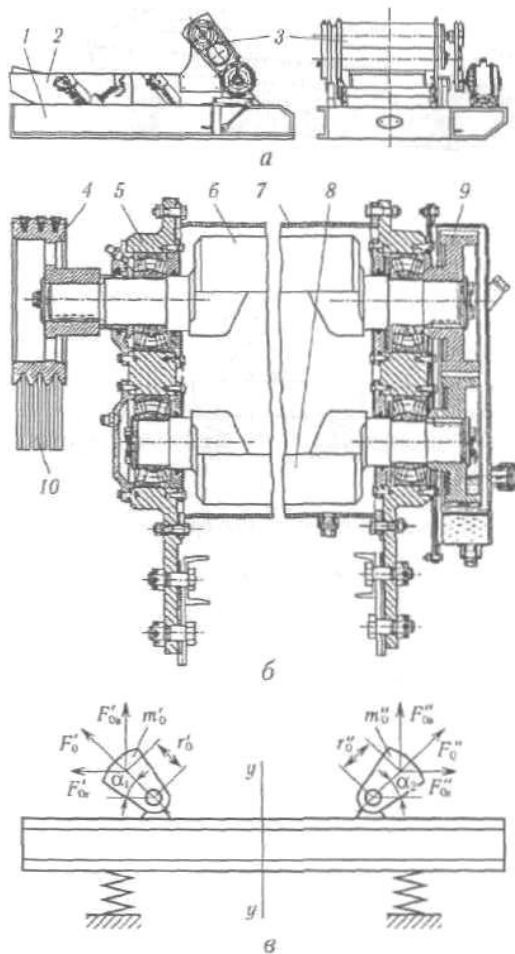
Горизонтальний грохот із напрямленими коливаннями: а – загальний вигляд; б – вібробудувач; в – схема вібробудувач, встановленого на коробі грохота, 1 – корпус; 2 – короб; 3 – вібробудувач напрямленої дії; 4 – шків; 5 – роликопідшипник; 6 та 8 – паралельні дисбалансні вали; 7 – корпус; 9 – зубчаста передача; 10 – клинопасова передача
